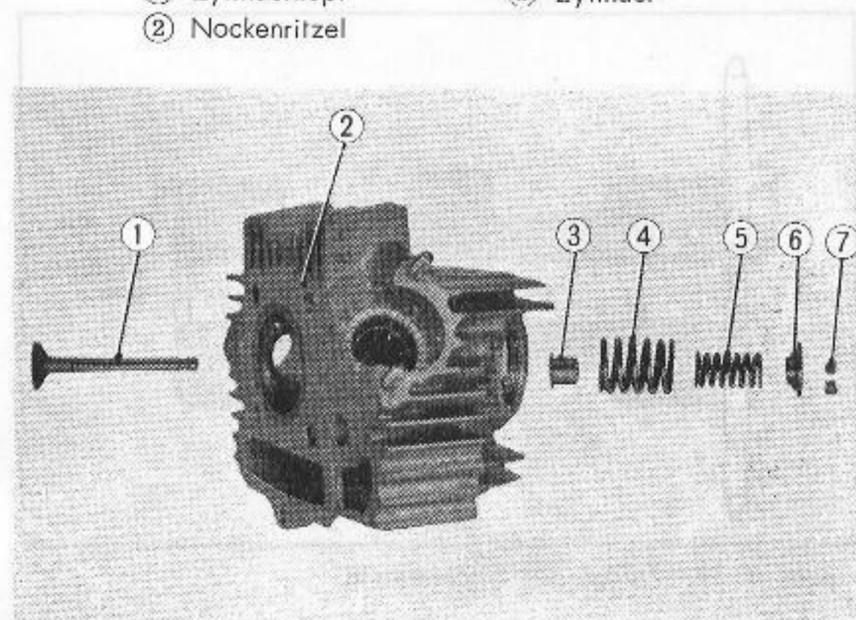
A Zylinderkopf mit Auslaßventil
